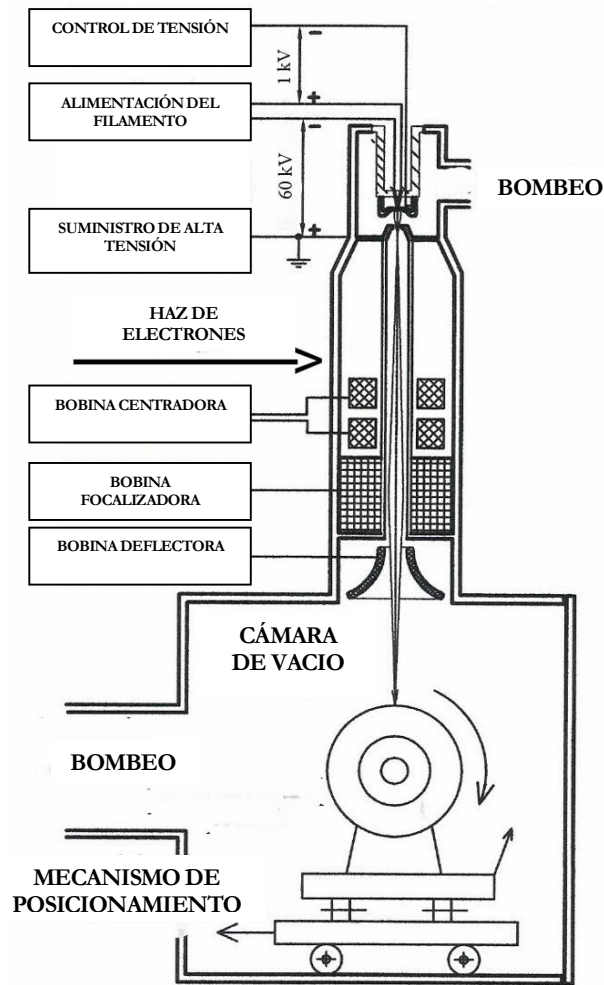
Instalación necesaria para la realización de una soldadura haz de electrones [115].
